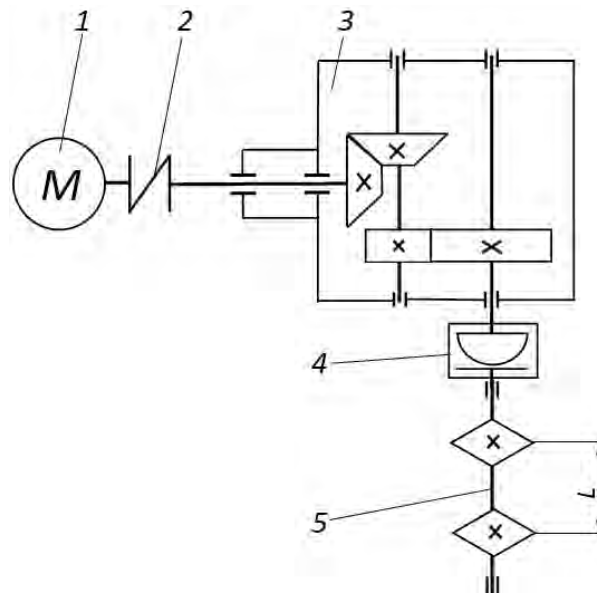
Схема привода цепного конвейера (вид сверху): 1 – асинхронный электродвигатель; 2 – муфта упругая втулочно-пальцевая; 3 – редуктор двухступенчатый коническо-цилиндрический (с конической передачей с круговым зубом и прямозубой цилиндрической тихоходной передачей); 4 – муфта зубчатая; 5 – приводной вал с двумя приводными звездочками
